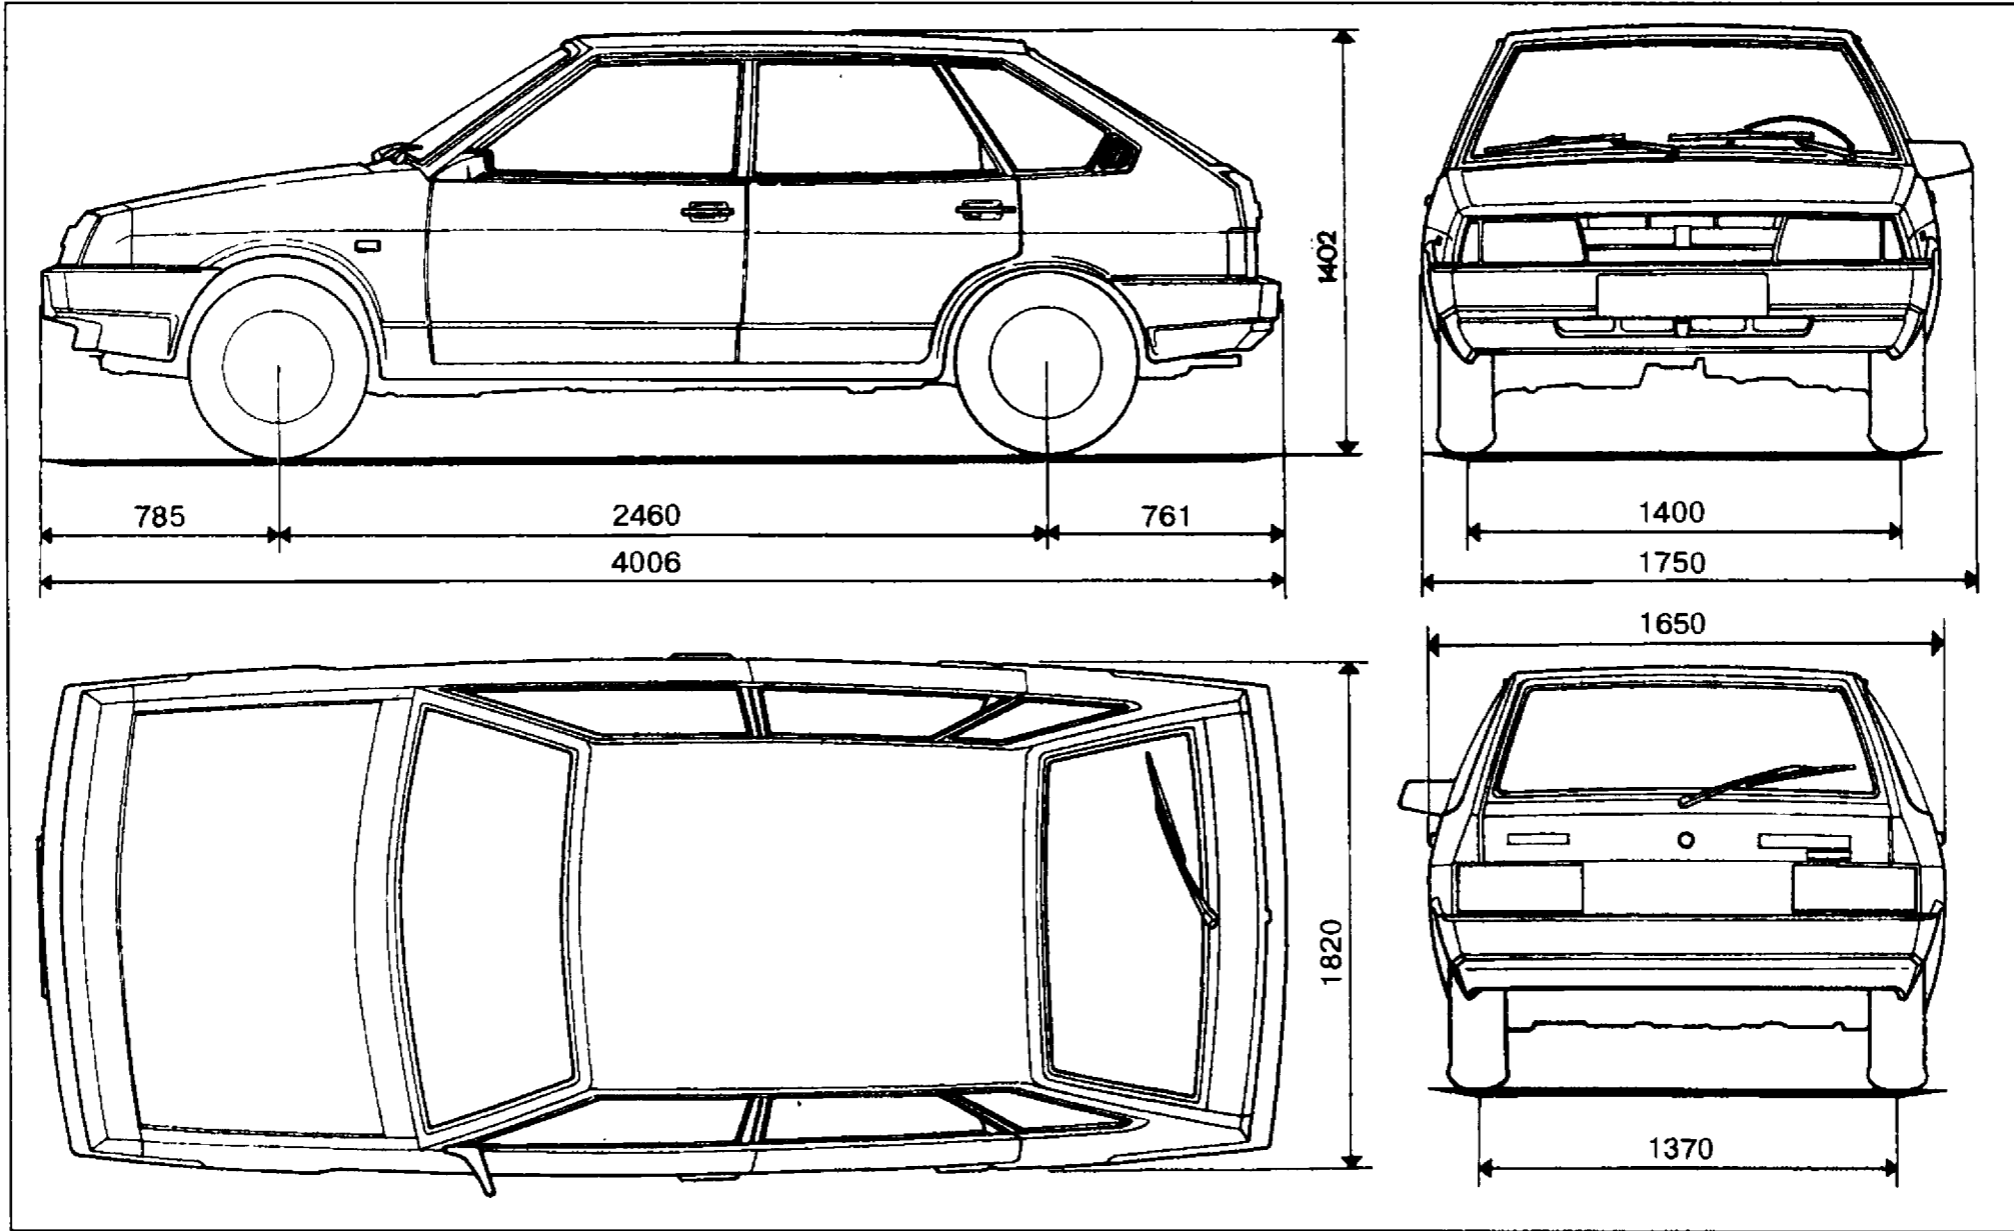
Габаритные размеры автомобиля ВАЗ-2109
